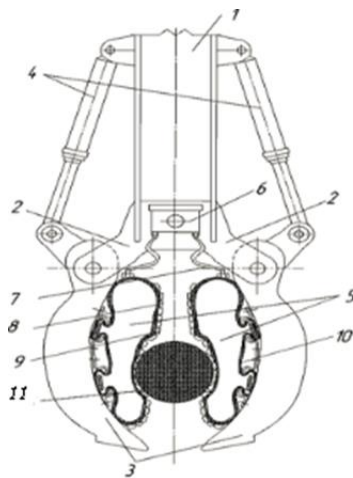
Робочий орган захвата, що адаптується до форми уламка
